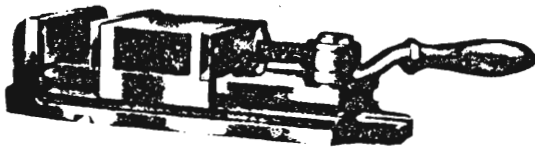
Tornillo de mordazas corriente (Cincinnati Milling Machine Co.)
